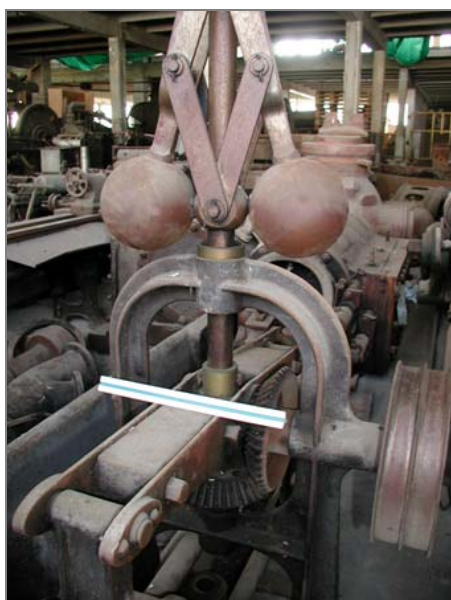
MACHINE PIGUET N°135 : PARTIE REGULATEUR A BOULES
